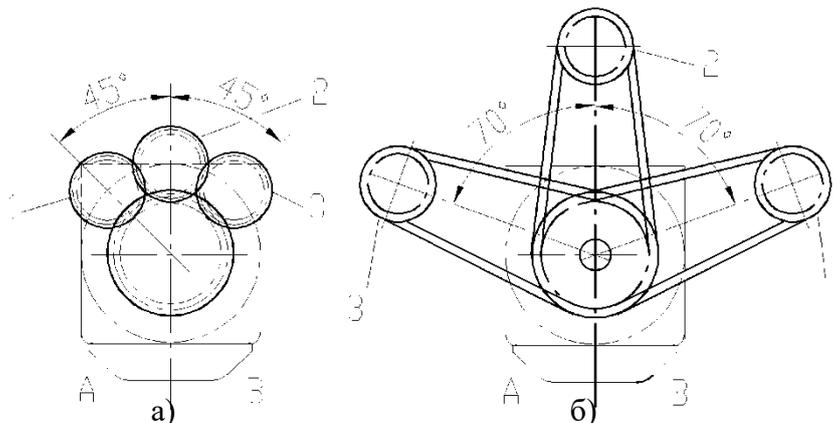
Схема выбора оптимального угла установки зубчатой (а) и клиноременной (б) передачи (Вид со стороны вала).
